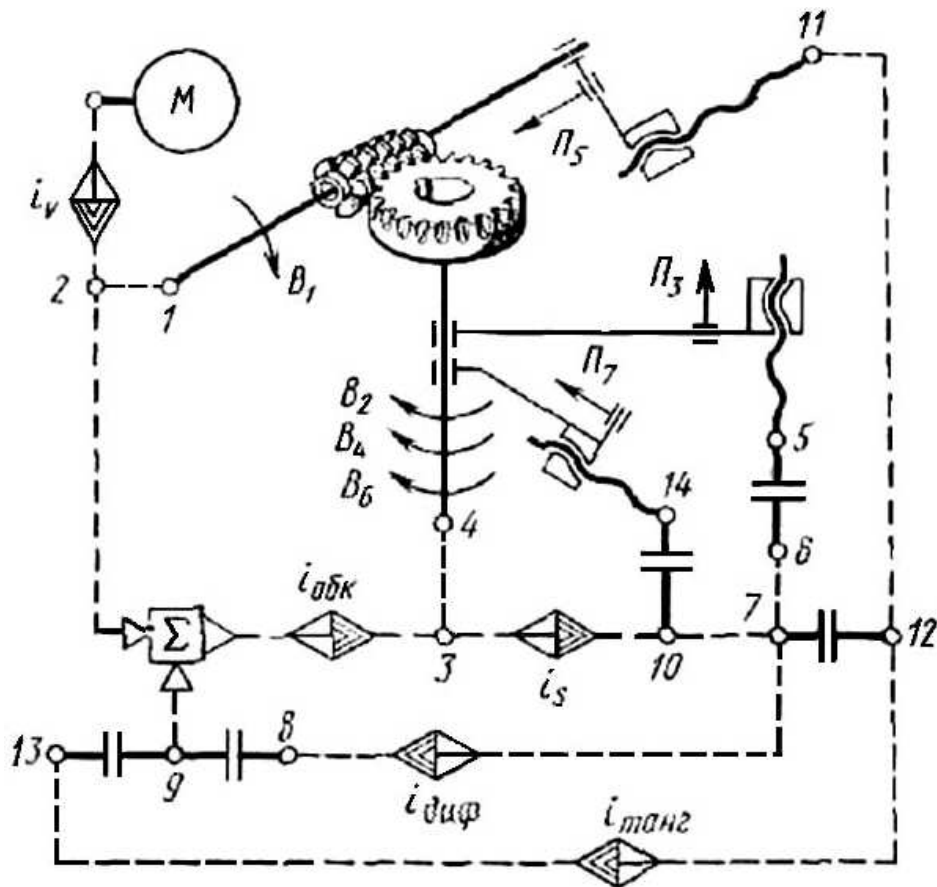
Кинематическая структура универсального зубофрезерного станка
